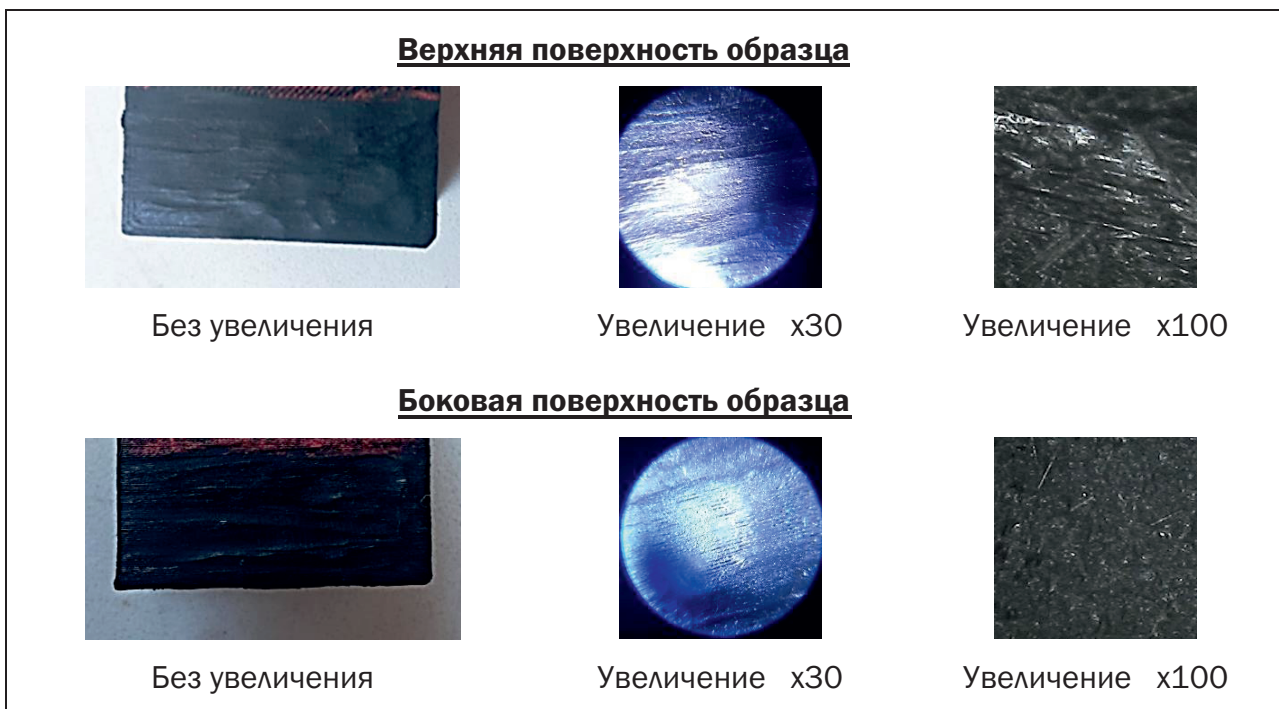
Часть заготовки, обработанная полировальным кругом с абразивной пастой
